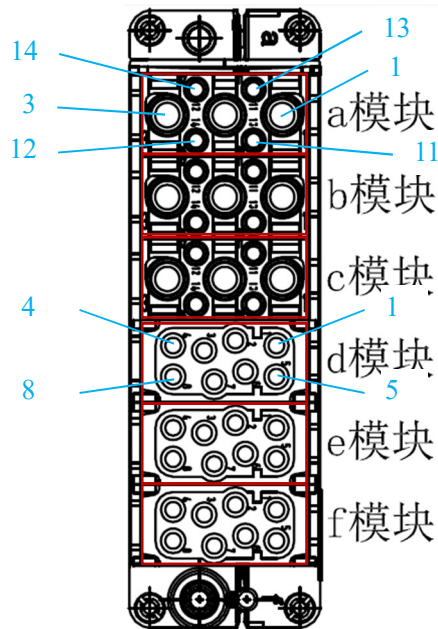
50KG-500KG 六轴 MOTOR 重载连接器外观图
